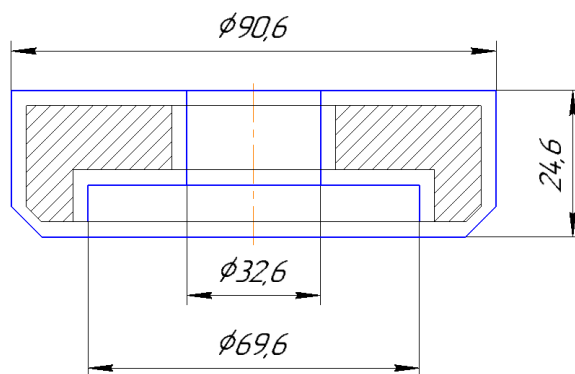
Ескіз заготовки деталі "Дорн"
